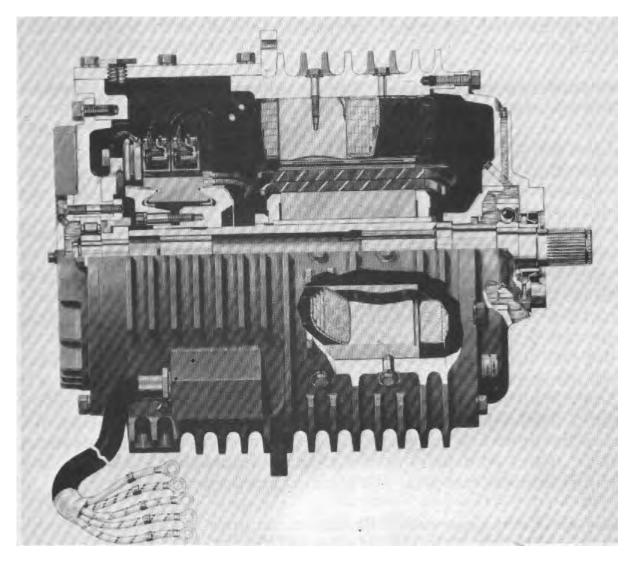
Motor típico a prueba de explosión para minas, de 20hp con 250Vcd.
